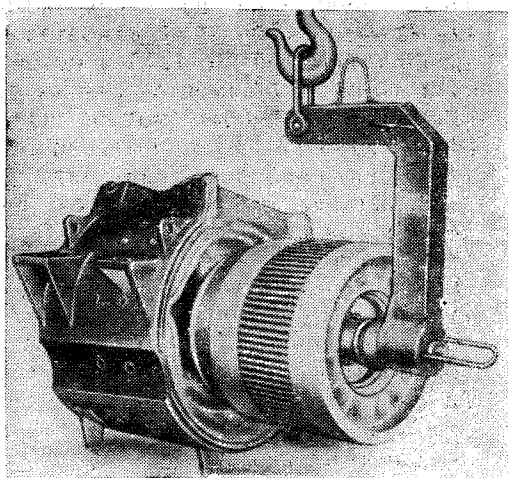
Сборка тягового двигателя электровозов ЧС с помощью монтажной скобы
